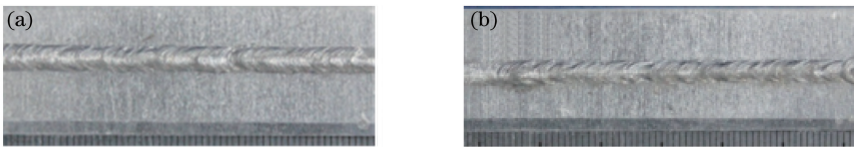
不同送丝角度下的焊缝表面成形。(a) 30° ; (b) 60°
